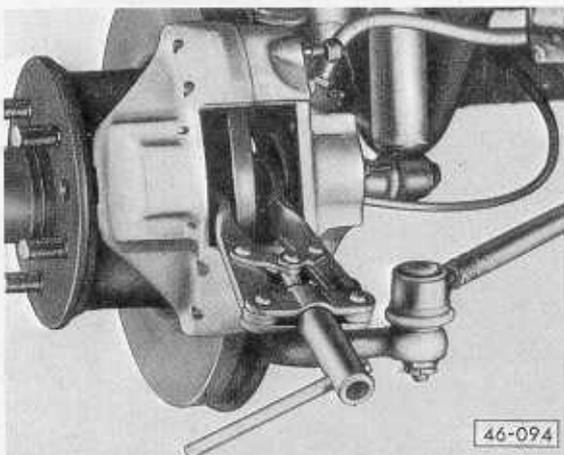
Kolben mit der Kolbenrücksetzvorrichtung zurückdrücken.
